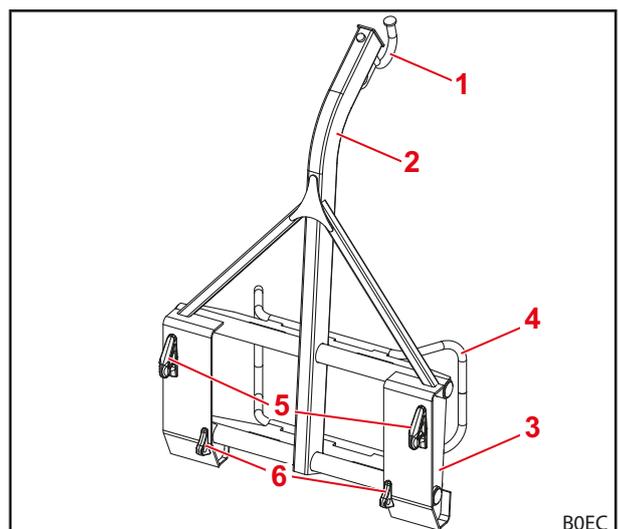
Estrutura do elevador de bigbag – Vista traseira
